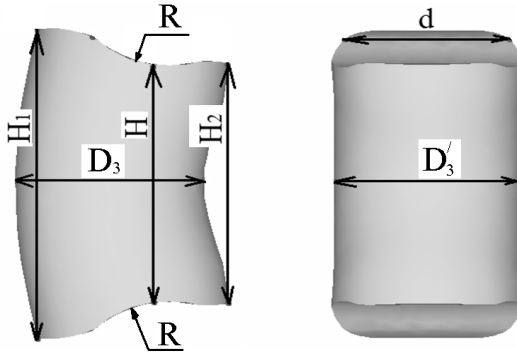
Твердотільна модель заготовки після осаджування $H_0/D_0 = 2,0$
